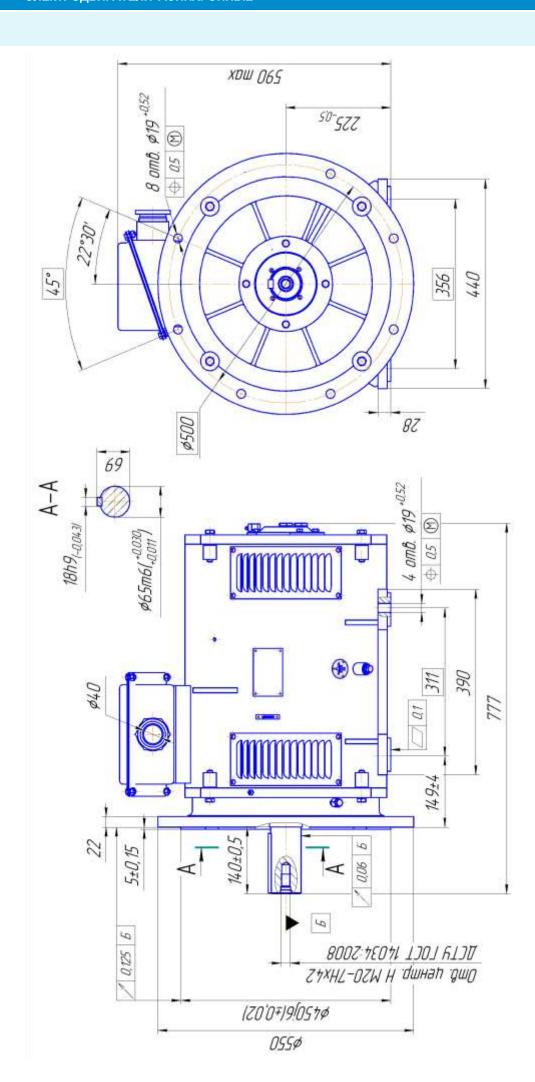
Габаритные, установочные и присоединительные размеры двигателя 4AЧ225M6. Масса двигателя (400 ± 20) кг
